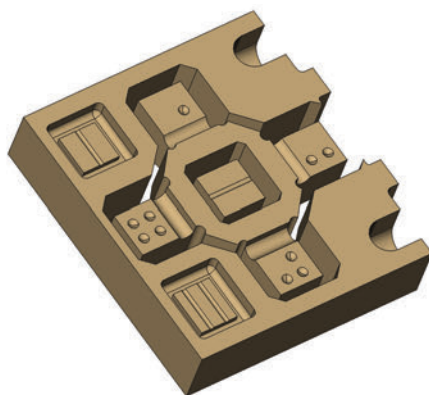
PIÈCE DE PARAMÉTRAGE/CONTRÔLE USINÉE PAR LA MACHINE N4 IMPRESSION
